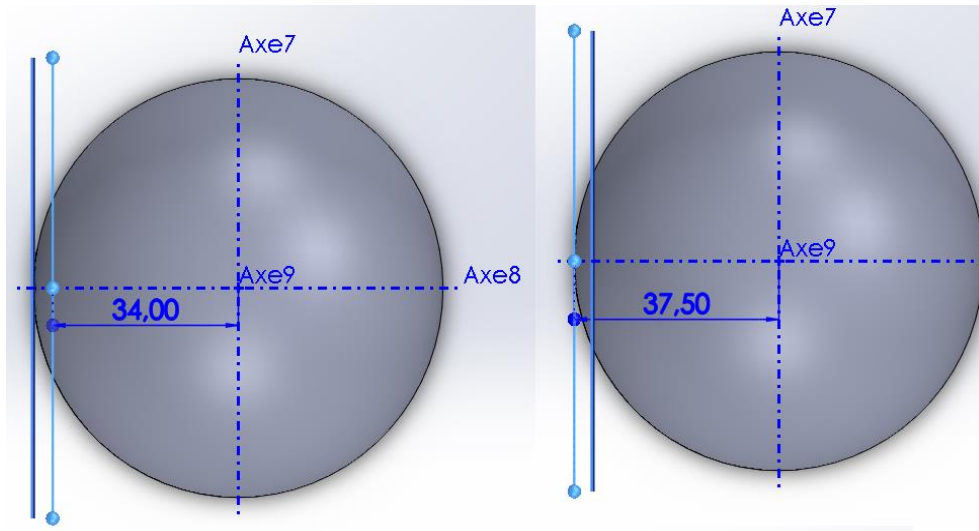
Création du deux nouveau plan parrèle au plan de face
